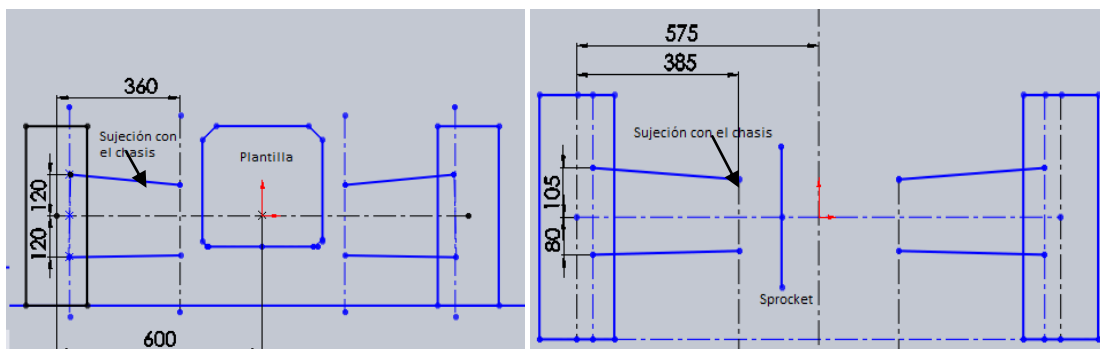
Vista frontal. Imagen izquierda suspensión frontal, sujeción con el chasis y upright.
